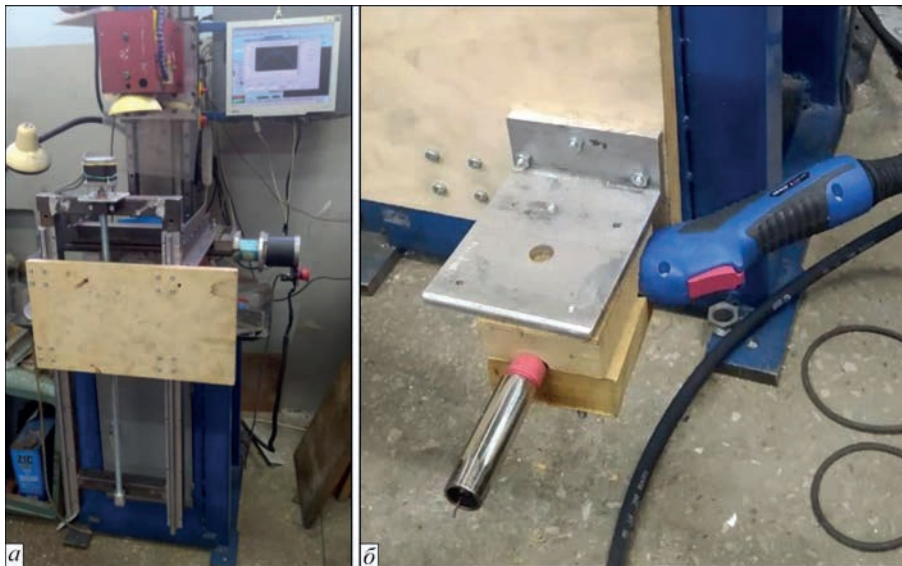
Установа із трикоординатним переміщенням зварювального інструменту: *a* – система переміщення; *б* – кріплення зварювального інструменту
